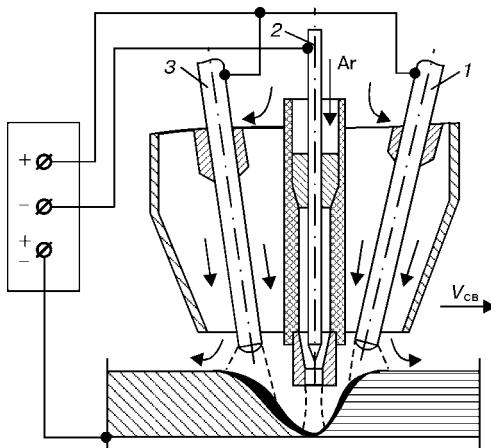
Схема процесса плазменной и дуговой сварки «гидра» (обозначения поз. 1–3 приведены в тексте)
